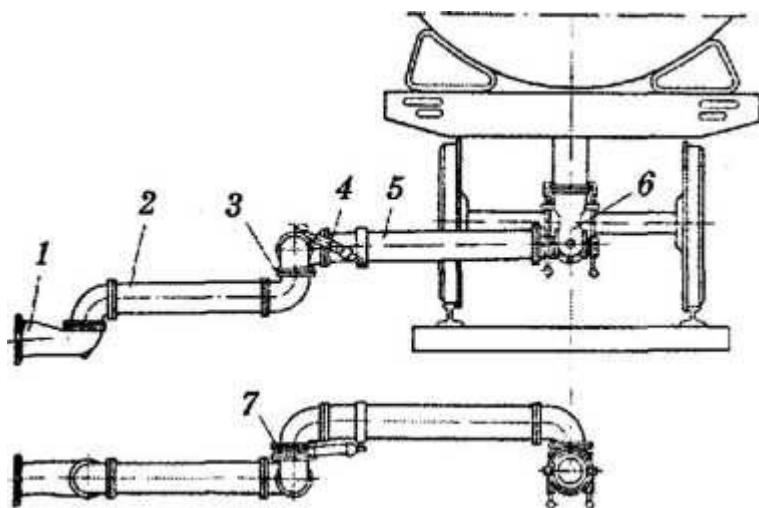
Принципиальная схема установки АСН-7Б: 1 - основание; 2 - труба коренная; 3 - шарнир горизонтальный; 4 - пружинное устройство; 5 - труба концевая; 6 - присоединительная головка; 7 - шарнир вертикальный
